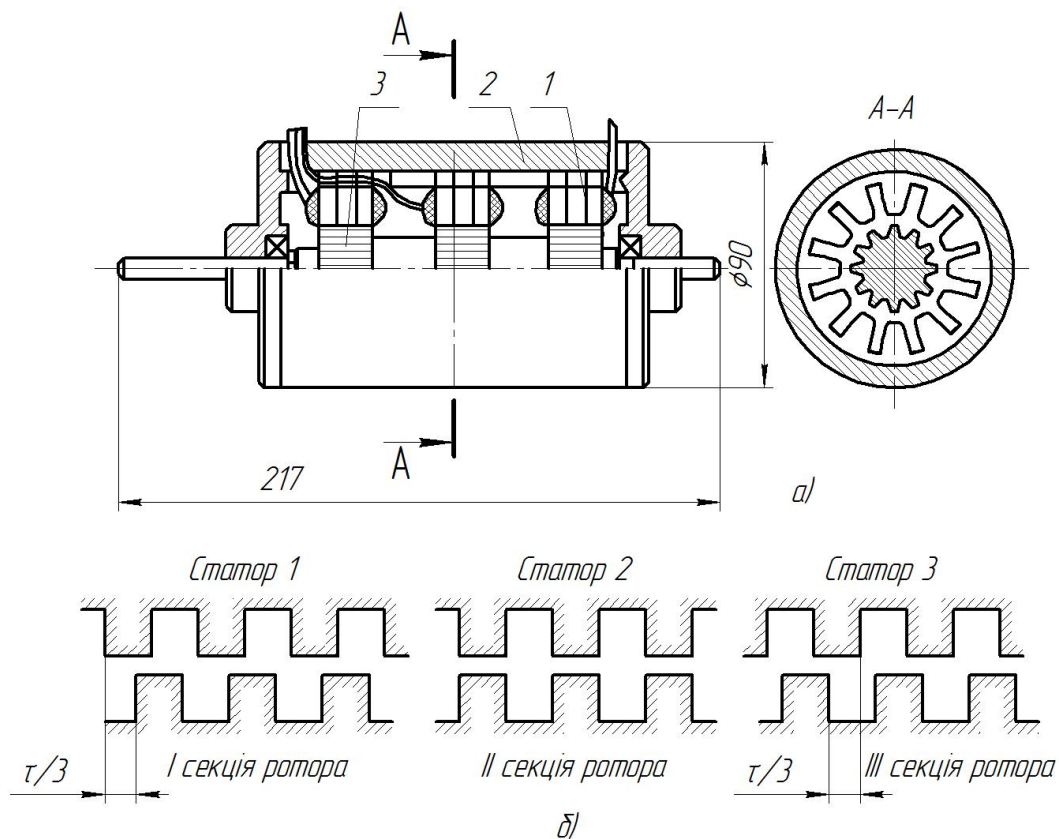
Кроковий двигун: а) – конструкція; б) – схема
